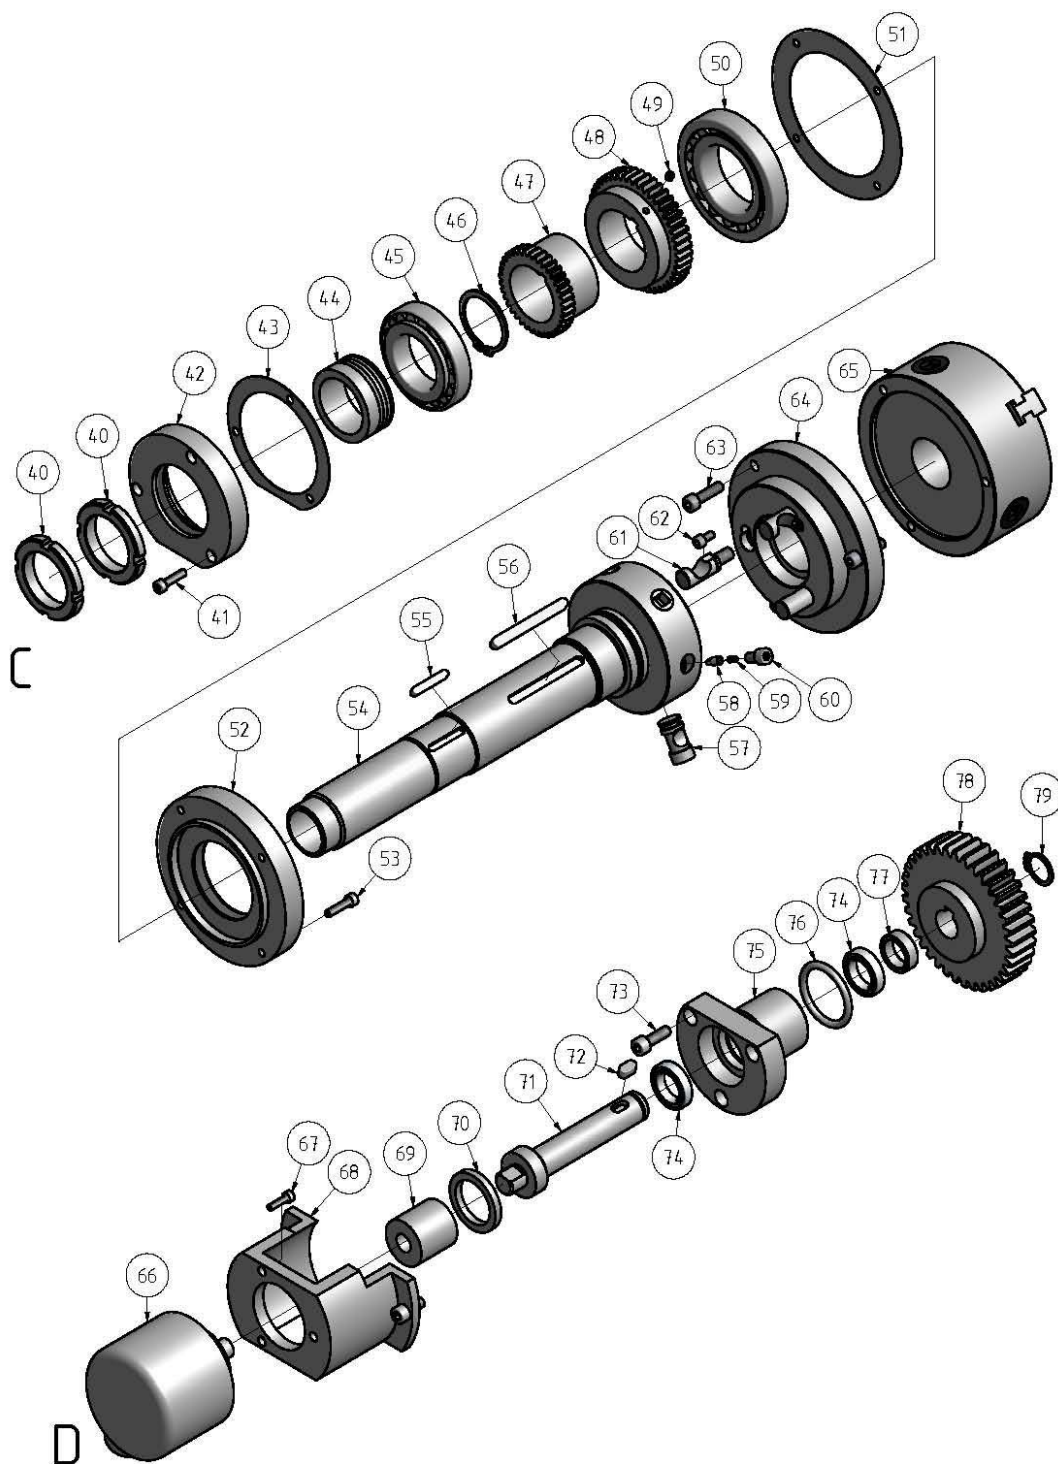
Getriebe Spindelstock 2-3 - Headstock gear 2-3
